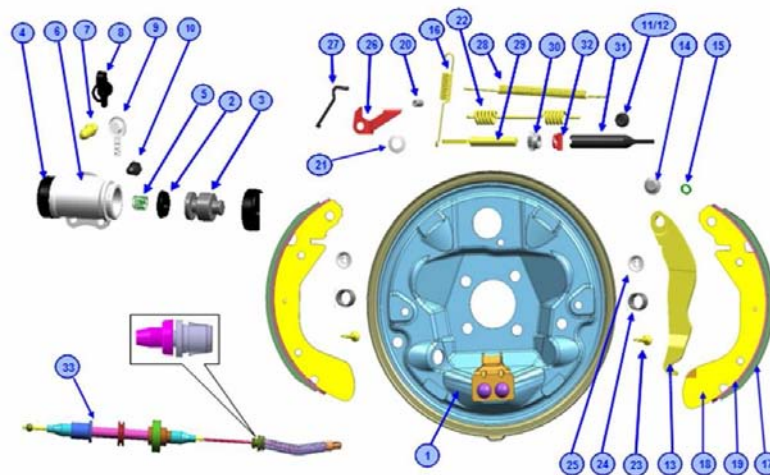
Vista explodida e relação de componentes principais do freio a tambor.
